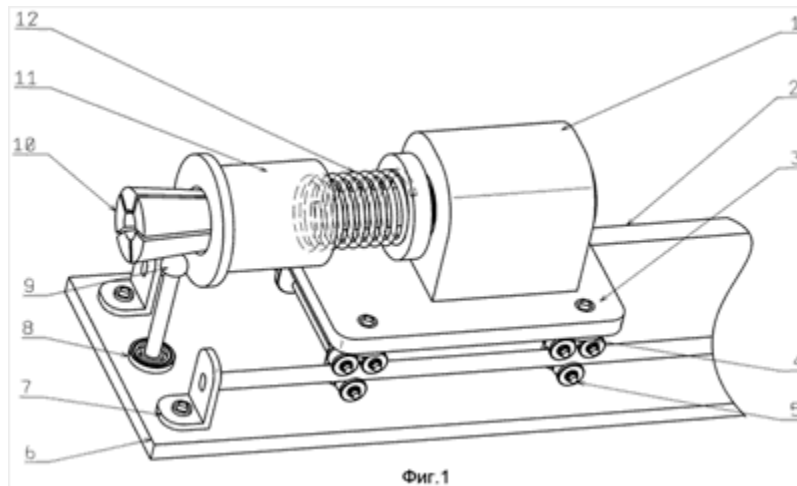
Внешний вид устройства в изометрической проекции
